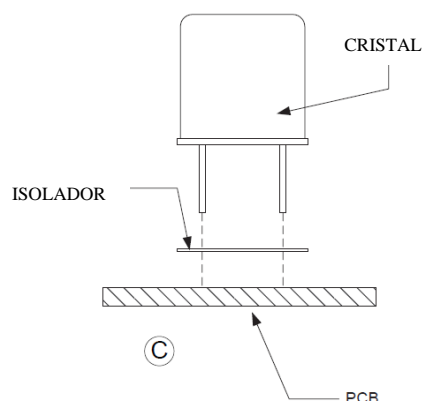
Utilização de isolador para montagem do cristal num PCB [9]
